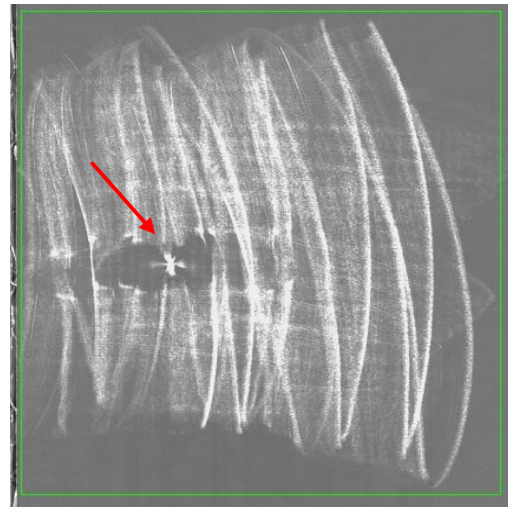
Puijsteen constras test (ernstegraad 1-2)
